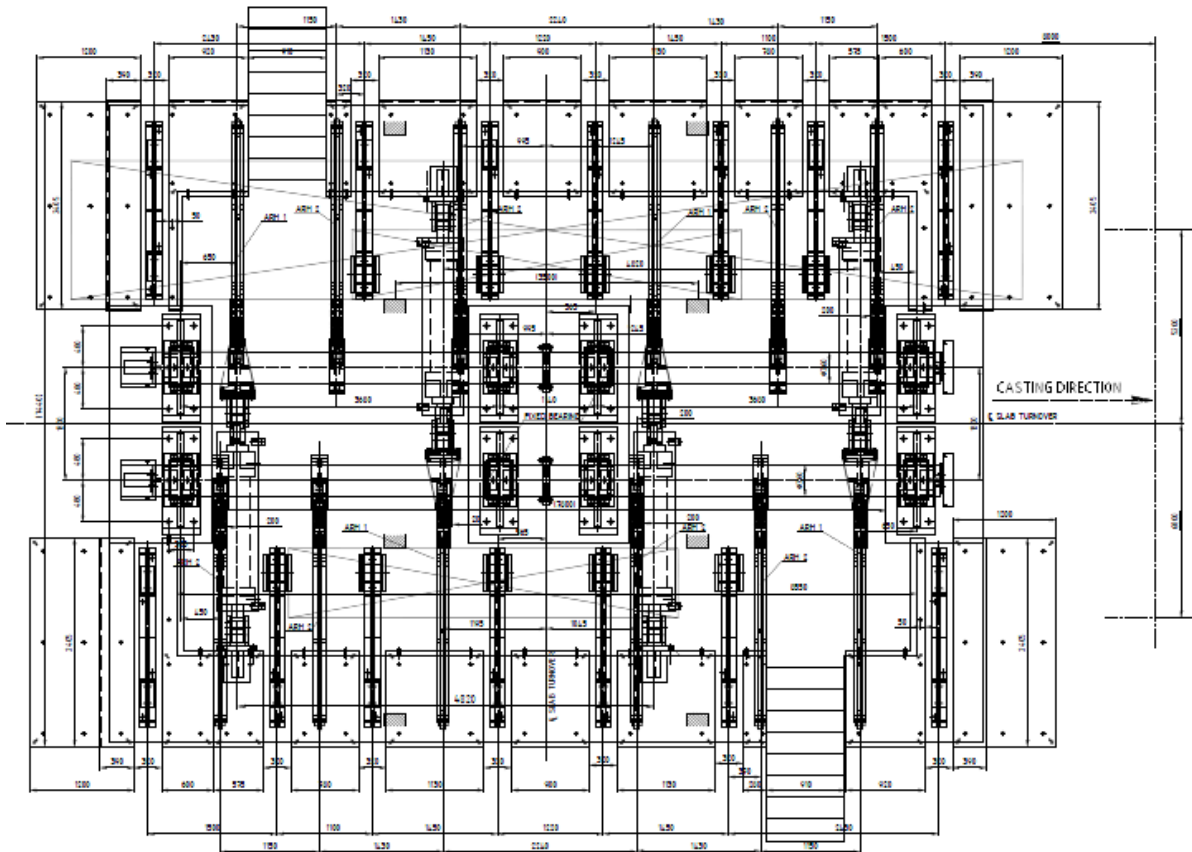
Grundriss eines Brammenwenders<sup>2</sup>
